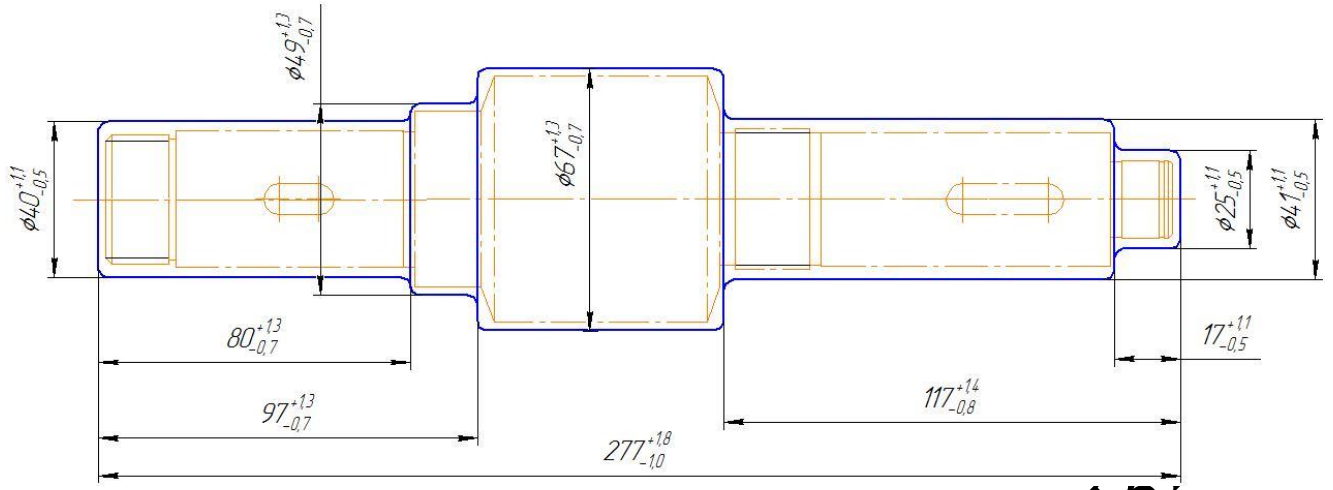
Заготовка отримана штампуванням на КГШП
